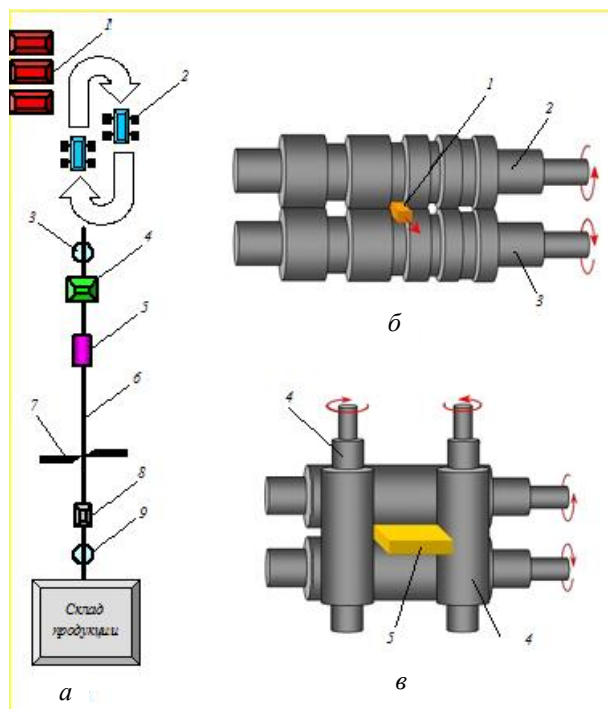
Блюминг и слябинг: *a* — расположение оборудования (1 — нагревательный колодец; 2 — слитковоз; 3 — весы для слитка; 4 — клеть дуо; 5 — машина огневой зачистки; 6 — рольганг; 7 — ножницы; 8 — клеймовщик; 9 — весы для сляба); *б, в* — схемы прокатки (2, 3 — горизонтальные рабочие валки; 1 — блюм; 4 — вертикальный валок; 5 — сляб)
